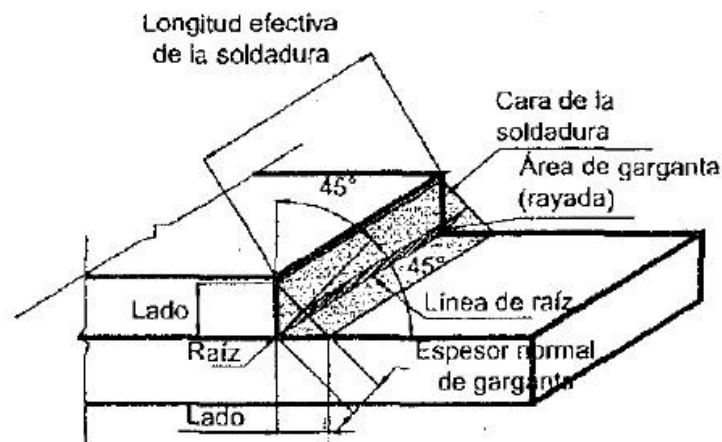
Nomenclatura soldaduras de filete S/CIRSOC 301-EL
